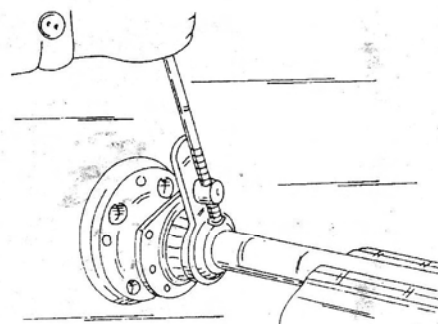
Отпускание или затяжка гайки крепления подшипника полуоси.
